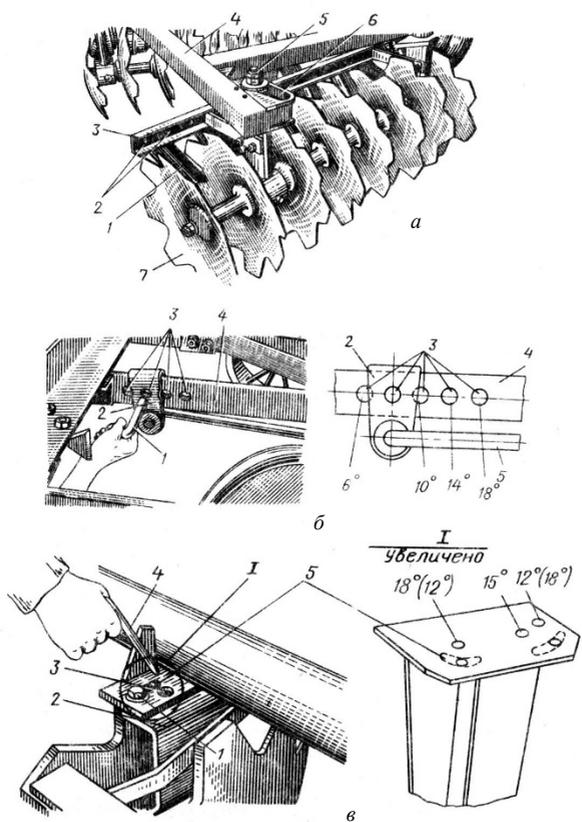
Регулировка угла атаки у борон: *а* – БДТ-7,0: 1 – чистик; 2 – прорези для установки чистиков; 3 – брус рамы; 4 – рама; 5 – регулировочные гайки; *б* – проушина; 7 – диск; *б* – БДТ-2,5: 1 – штырь; 2 – ползун; 3 – отверстия; 4 – брус; 5 – тяга; *в* – БДТН-2,2: 1 – болт; 2 – кронштейн; 3 – отверстие; 4 – штырь; 5 – паз
